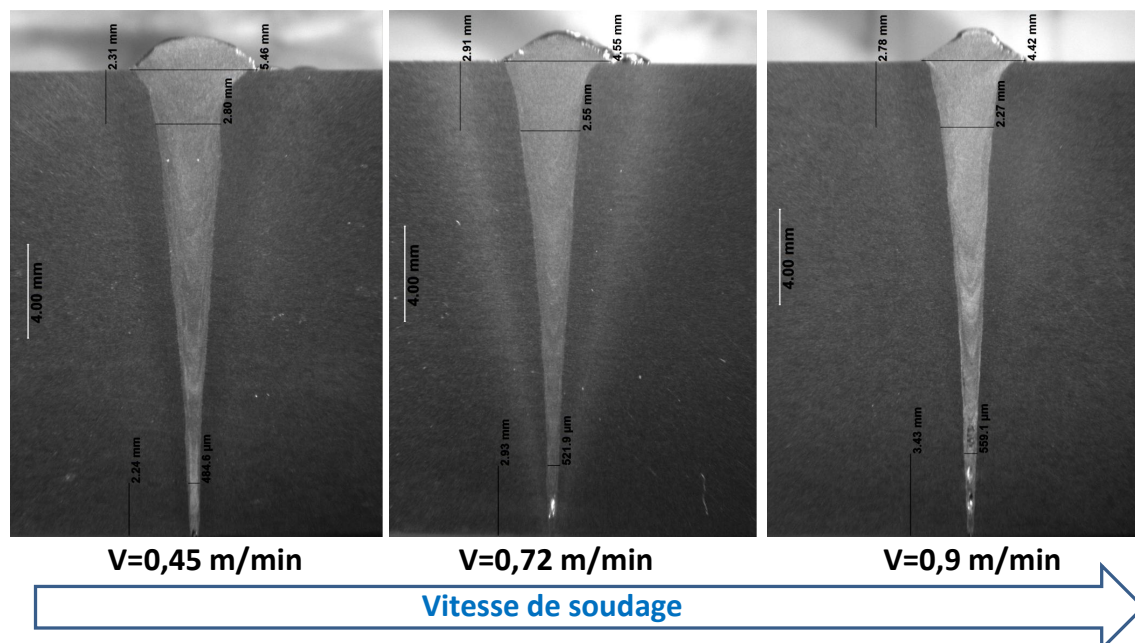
Macrographies obtenues sur les plaques soudées
